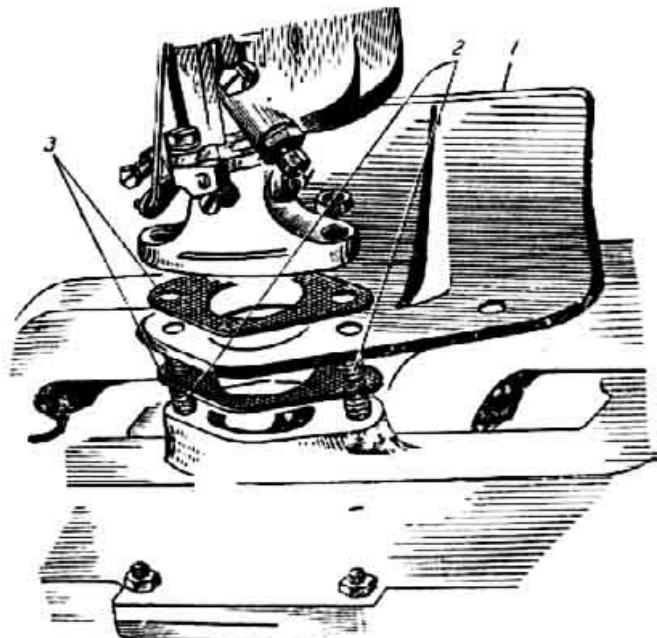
Крепление и установка козырька выхлопной трубы:
